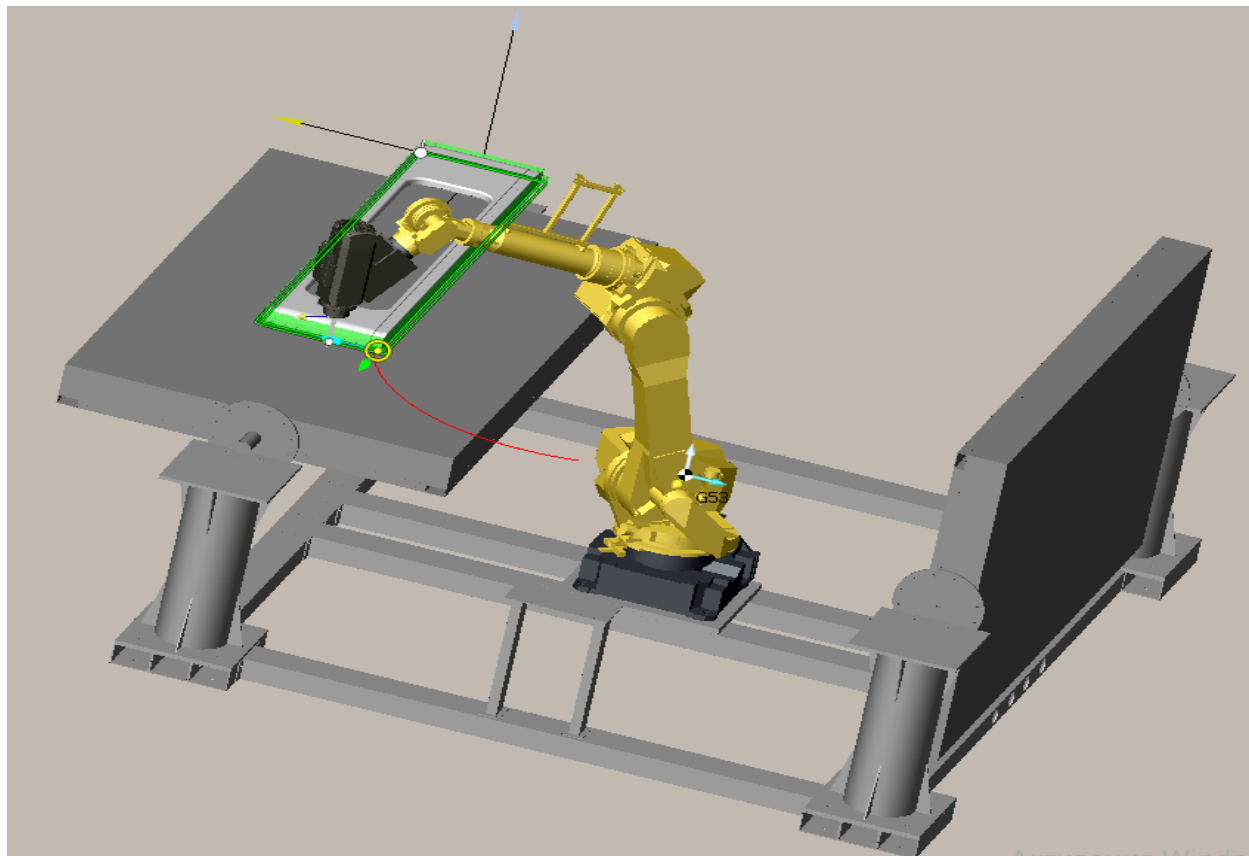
Робот-маніпулятор FANUC M-710iC/70
